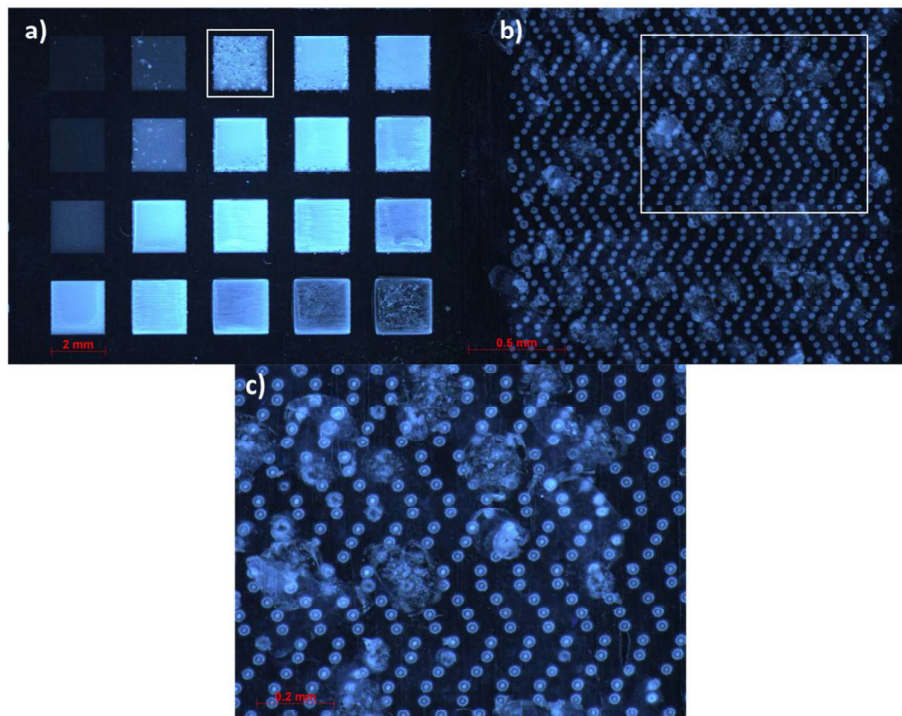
Fracture superficielle du PMMA en surface sous forme d’écaillage lors de la gravure laser par la machine laser IREPA, (a) zoom x20, (b) zoom x50, (c) zoom x100
